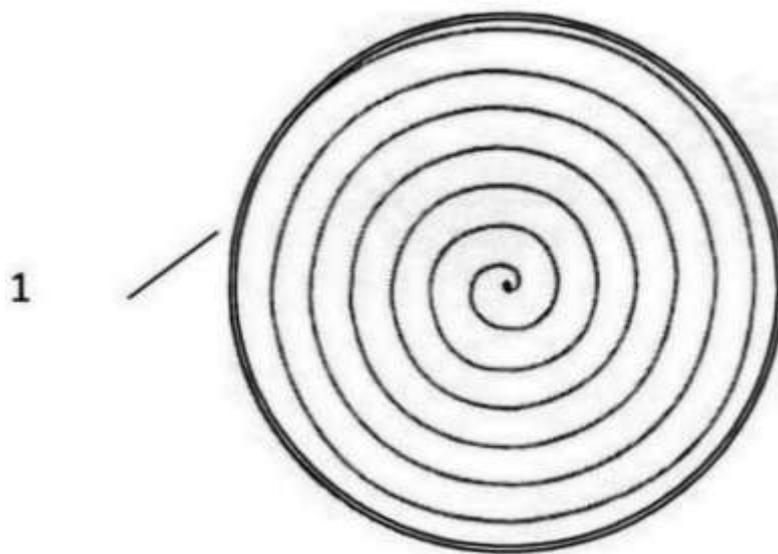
общий вид корпуса глушителя спирального без торцовых стенок и шумопоглощающего материала
